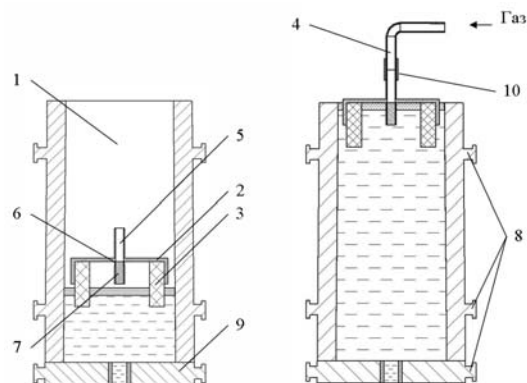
Схема устройства с плавающей вставкой из огнеупорного материала: 1 – литейная форма; 2 – металлический корпус; 3 – вставка из огнеупорного материала; 4 – газопровод; 5 – газоподающий патрубок; 6 – отверстия; 7 – газопроницаемая пробка; 8 – цапфы; 9 – поддон; 10 – муфта.
